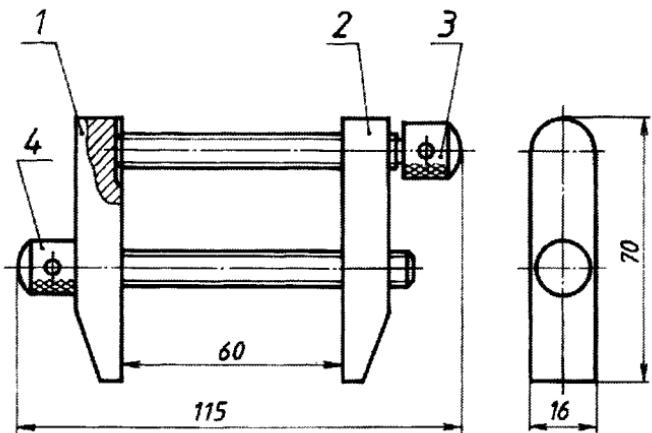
Струбцина скобообразная. Сборочный чертеж
